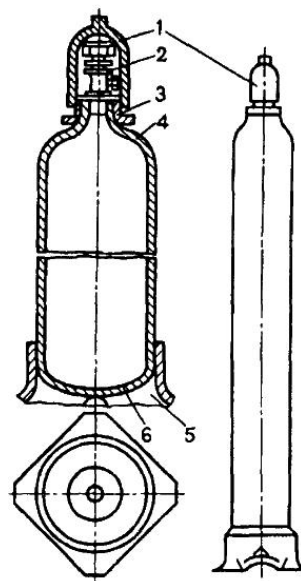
Конструкція кисневого балону: 1 – захисний ковпак; 2 – запорний вентиль; 3 – кільце; 4 – горловина; 5 – башмак; 6 – дно балону.
